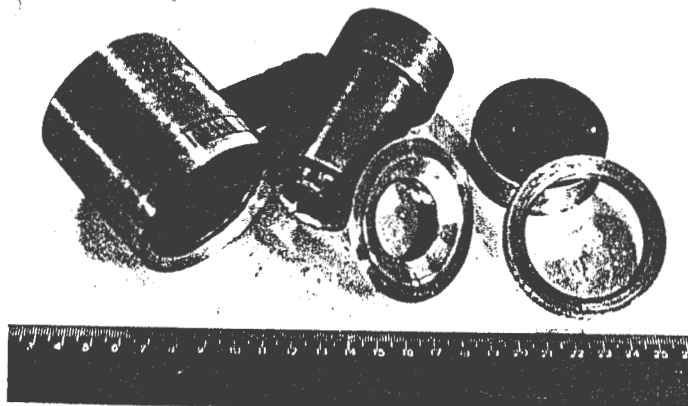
Fotografia do bocal MIG/MAG de soldagem subaquática
